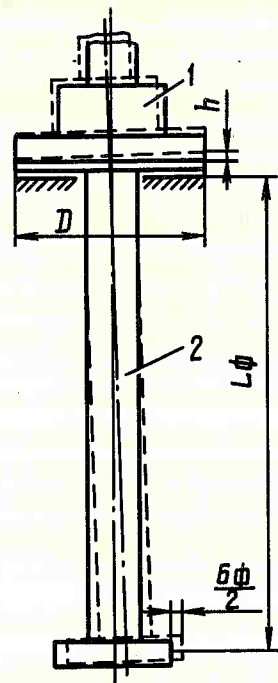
Расчет клина, снимаемого с тыльной стороны диска подпятника или с опорной плоскости втулки: 1 — втулка подпятника; 2 — вал (штриховой линией показано положение вала после установки клиновидной прокладки высотой h)
